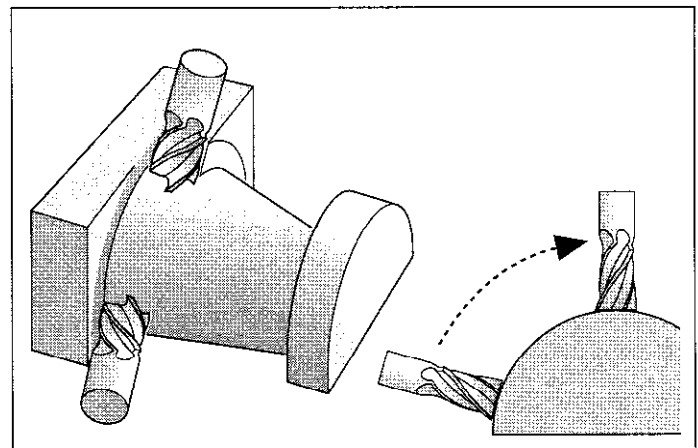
Gleichzeitiges Verfahren von mehr als drei Koordinatenachsen, z.B. Bearbeiten einer 3D-Form mit Schaftfräser
